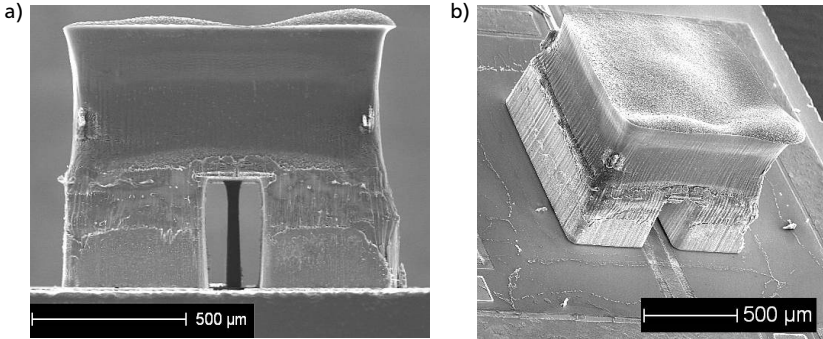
Technologie-Demonstrator mit der Probenbezeichnung Probe FG316 O10 aus dem Prozessstrang *UV LIGA*: a) Seitenansicht, b) schräge Draufsicht.
